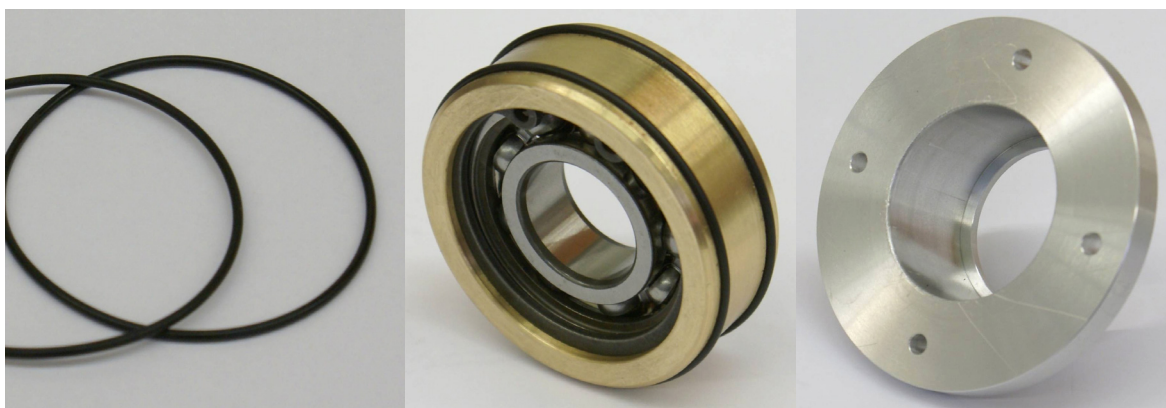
Einbau der Fanglager mit Elastomerringen, [QWLK07]
